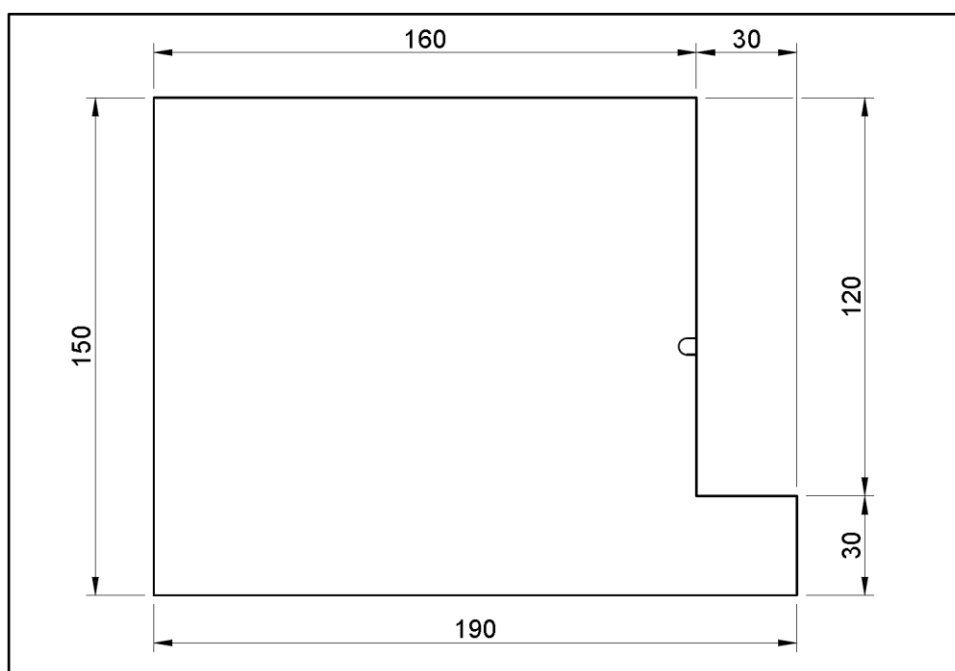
Desenho do dimensional dos corpos de prova.
